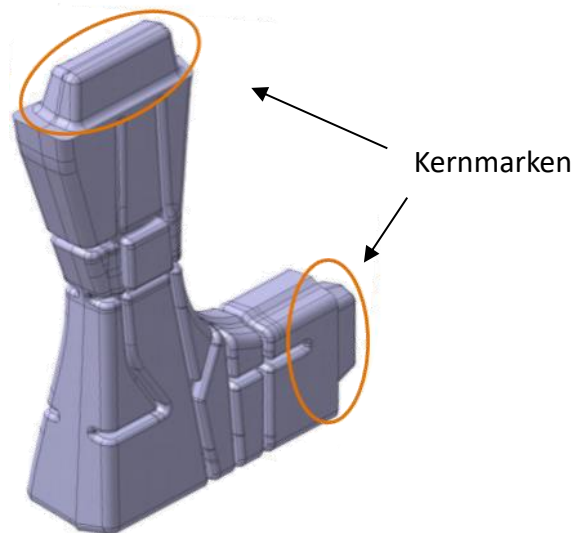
Schematische Darstellung der Werkzeugoberfläche mit eingebrachter Rillenstruktur zur Fixierung des Salzkerns im Umgusswerkzeug
